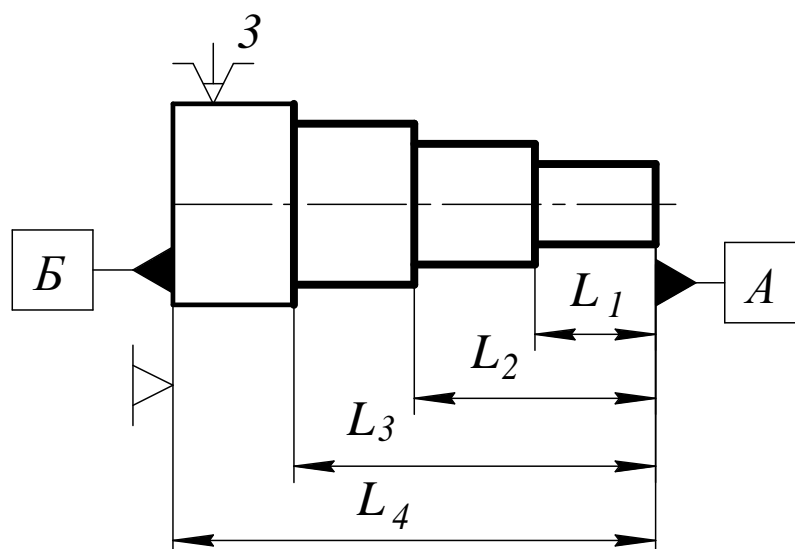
Пример нанесения размеров от измерительной базы, координирующей положение на детали нескольких поверхностей
